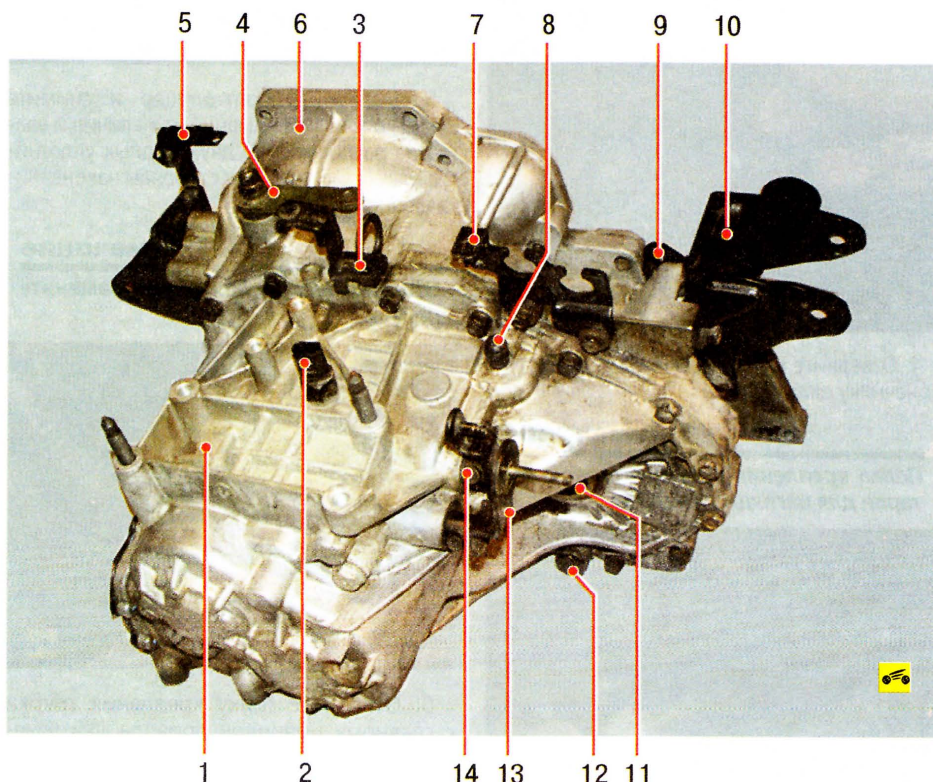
Механическая коробка передач: 1 – картер коробки передач; 2 – выключатель света заднего хода; 3 – кронштейн крепления полки аккумуляторной батареи с транспортной проушиной; 4 – рычаг вилки выключения сцепления; 5, 10 – кронштейны опор подвески силового агрегата; 6 – картер сцепления; 7 – кронштейн крепления тросов управления коробкой передач; 8 – сапун; 9 – датчик скорости; 11 – сальник полуоси; 12 – пробка отверстия для слива масла; 13 – рычаг переключения передач; 14 – рычаг выбора передач
